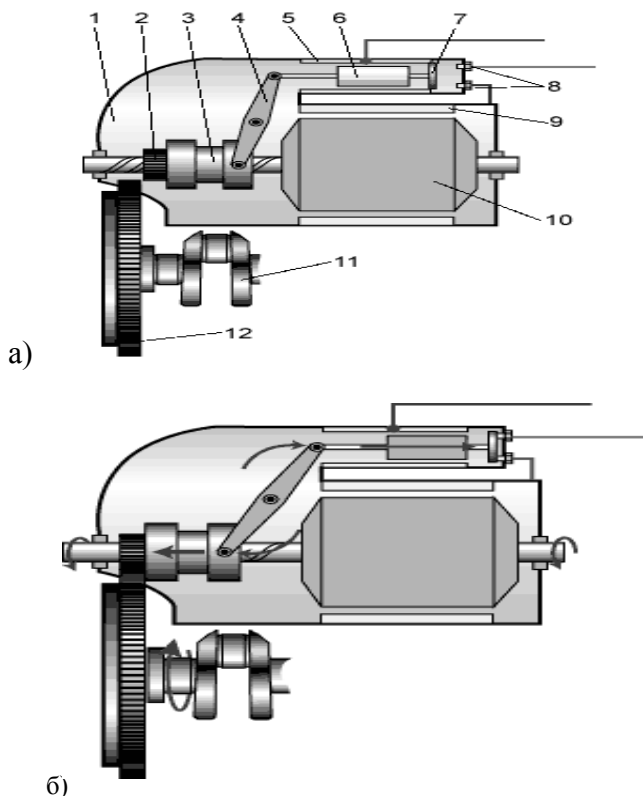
Схема системы пуска двигателя а) стартер выключен; б) стартер включен; 1 - корпус стартера; 2 - вал якоря стартера; 3 - шестерня привода с муфтой свободного хода; 4 - рычаг привода шестерни; 5 - обмотки тягового реле; 6 - якорь тягового реле; 7 - контактная пластина; 8 - контактные болты; 9 - обмотки стартера; 10 - якорь стартера; 11 - коленчатый вал двигателя; 12 - зубчатый венец маховика
